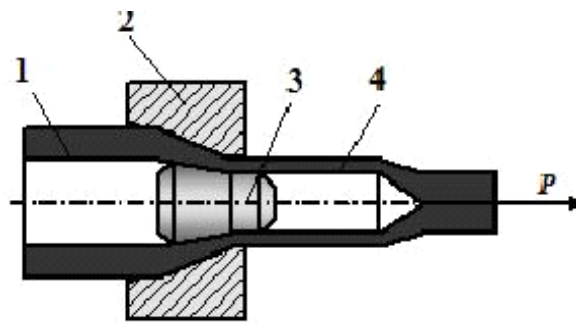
1 – заготовка; 2 – волока (фильера); 3 – изделие; 4 – плавающая оправка.
